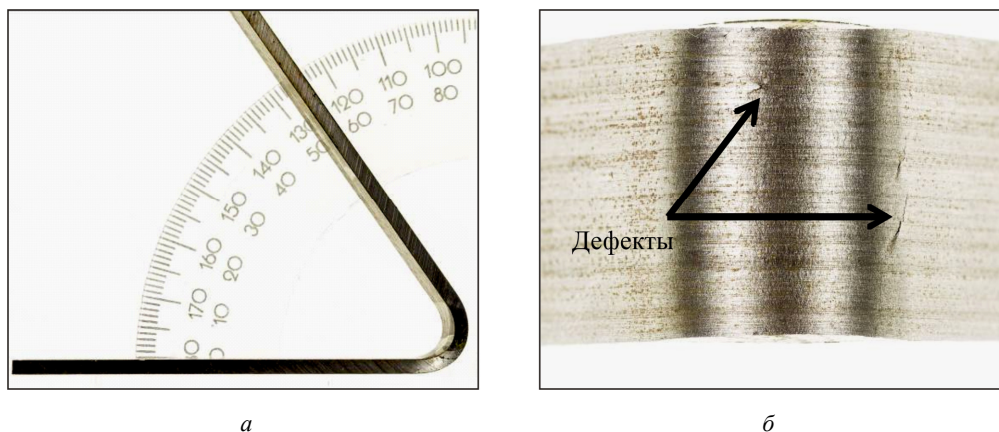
Испытание на трехточечный изгиб: *а* – внешний вид образца; *б* – трещины в зоне наплавляемого металла дефектного образца
